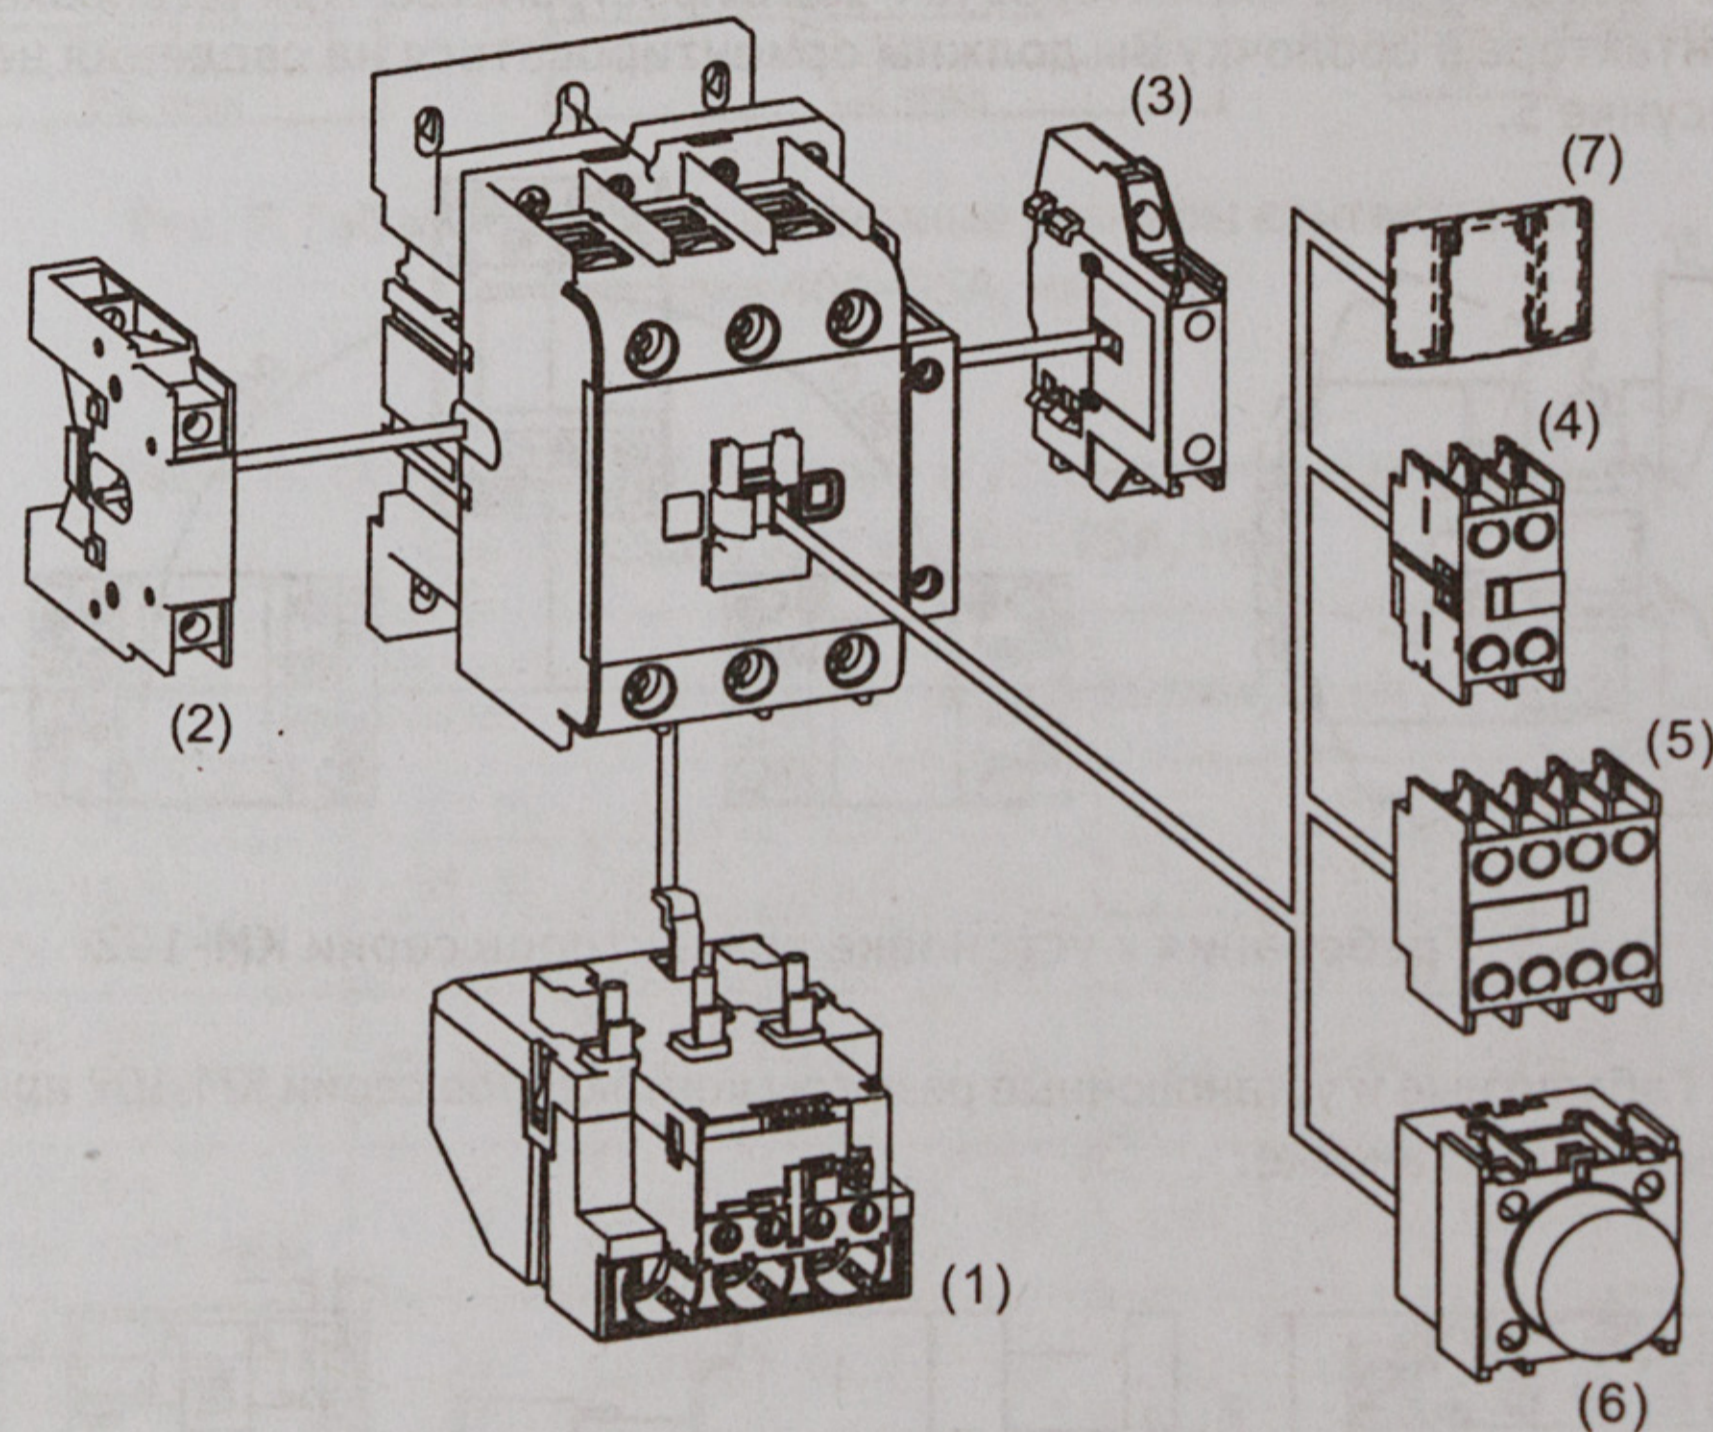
Контактор КМ-102 и схематическая установка аксессуаров
